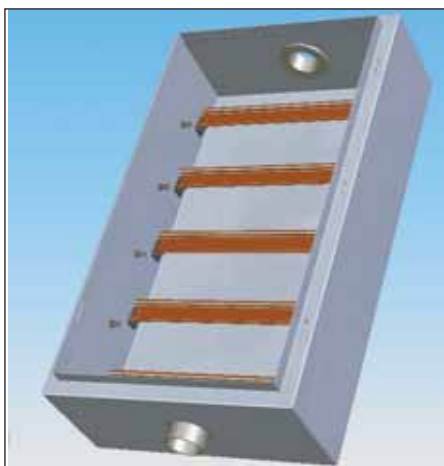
Корпус в исполнении для модульной конструкции с установленными стыковочными втулками и рейками для крепления аппаратов
